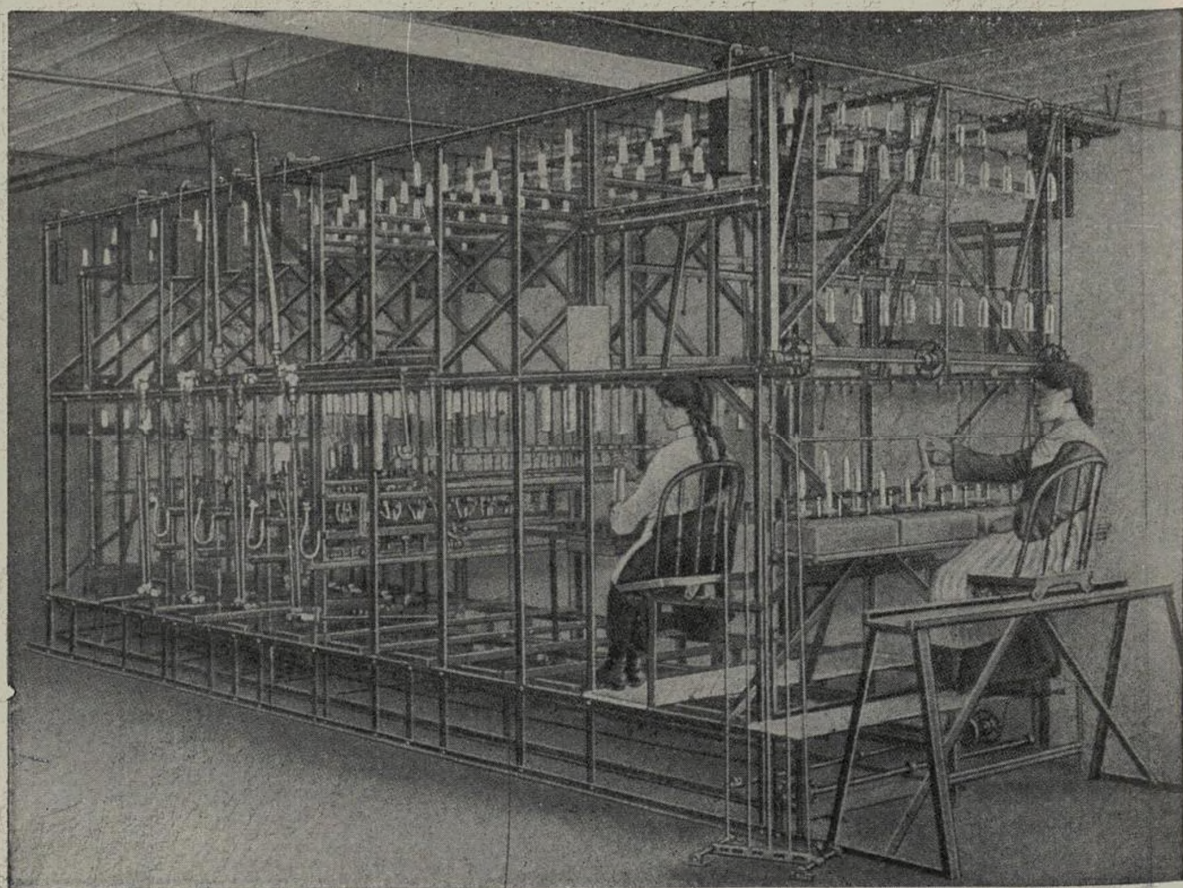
Machines à brûler de la Société Hella, à Hambourg.
